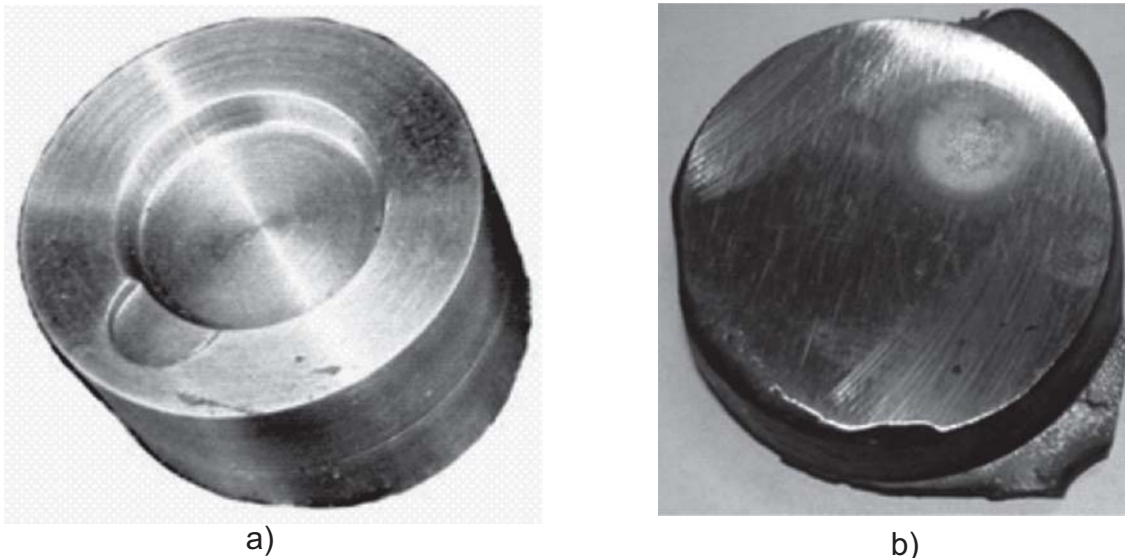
(a) Coquilla de fundición gris; (b) Muestra cilíndrica de F-G de 40 mm de diámetro.
